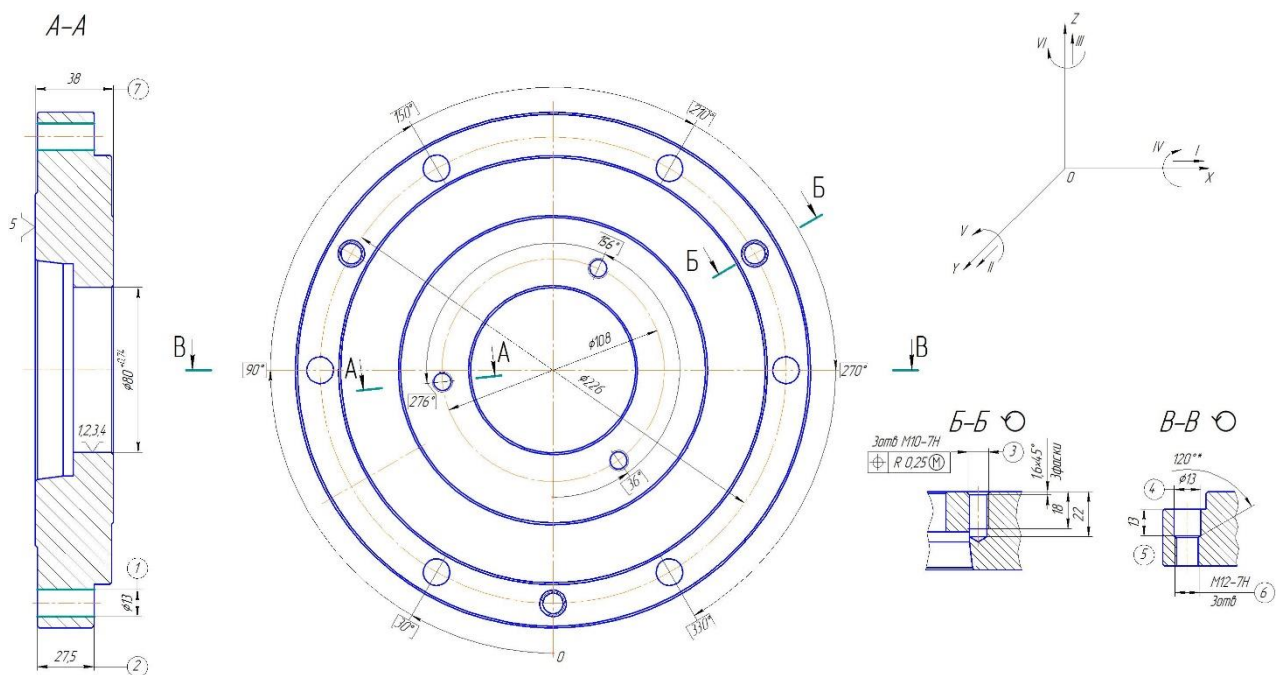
Схема базування заготовки в спеціальному пристосуванні
